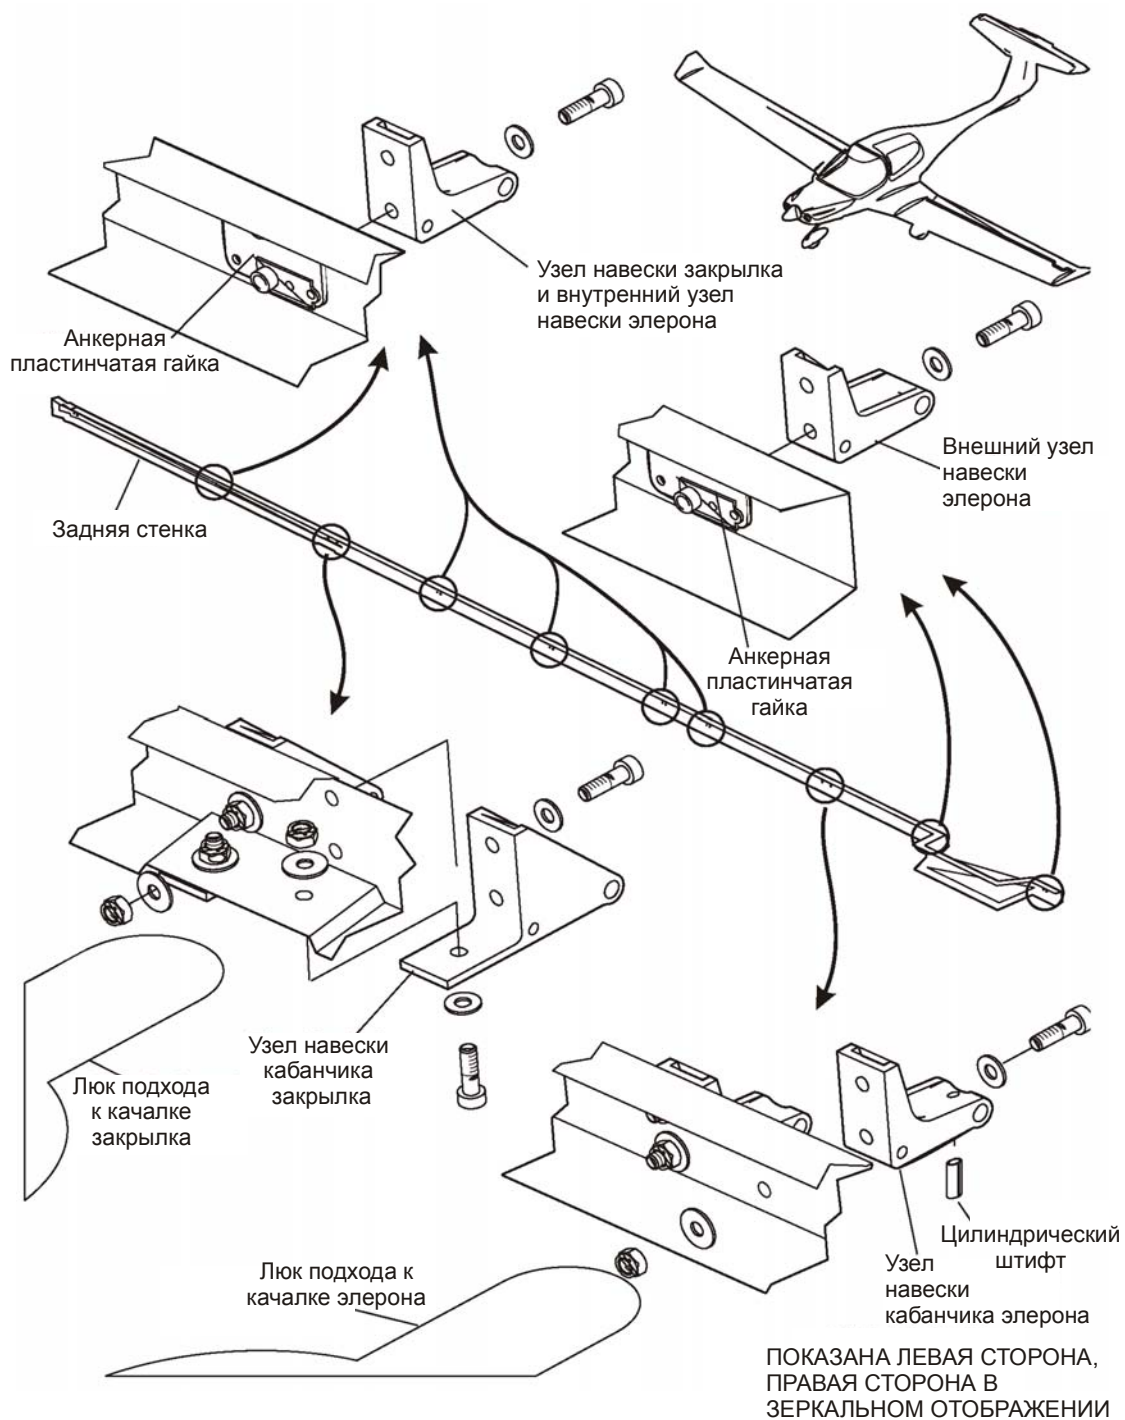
Установка кронштейнов навески рулевых поверхностей
